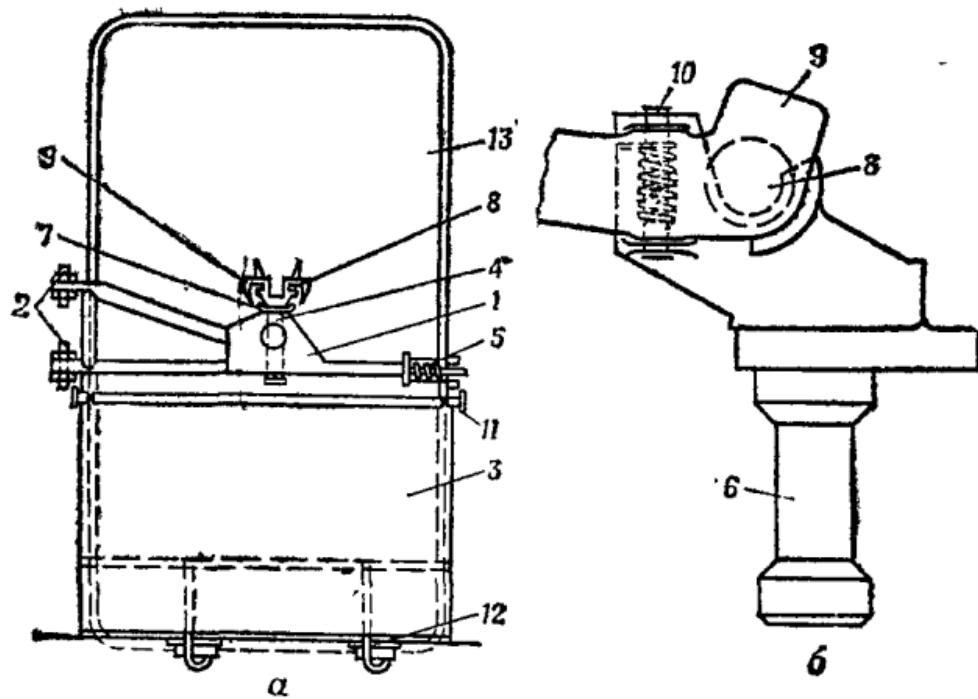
Шкворневая установка для стрельбы через входную дверь:
